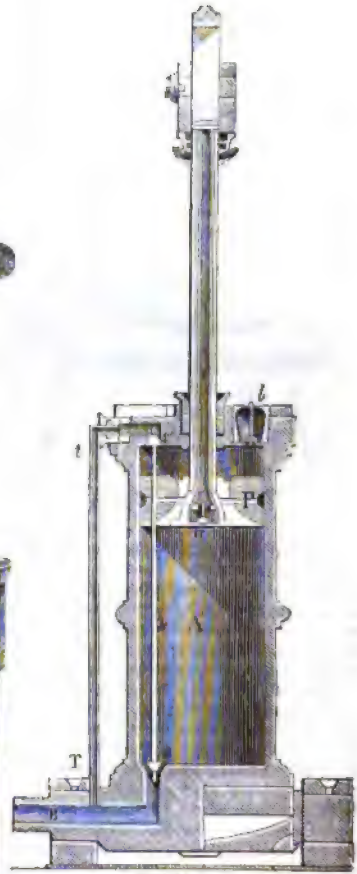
Corps de pompe de la machine de M. Bianchi.
